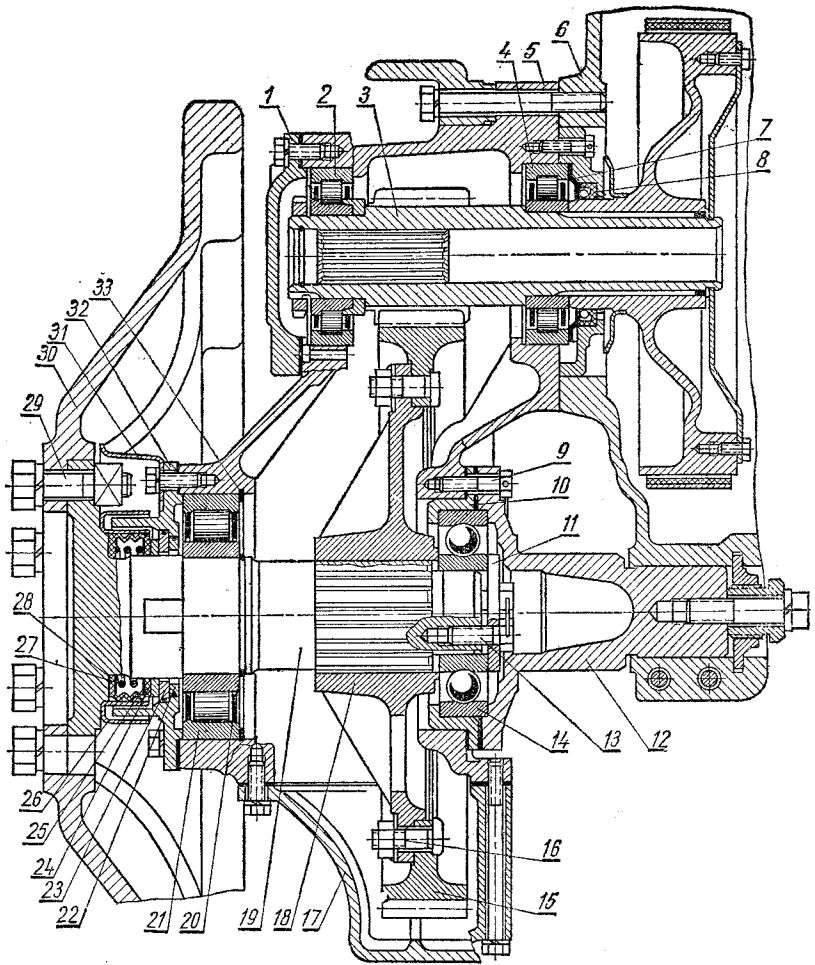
Конечная передача тракторов ДТ-75, ДТ-75М:
